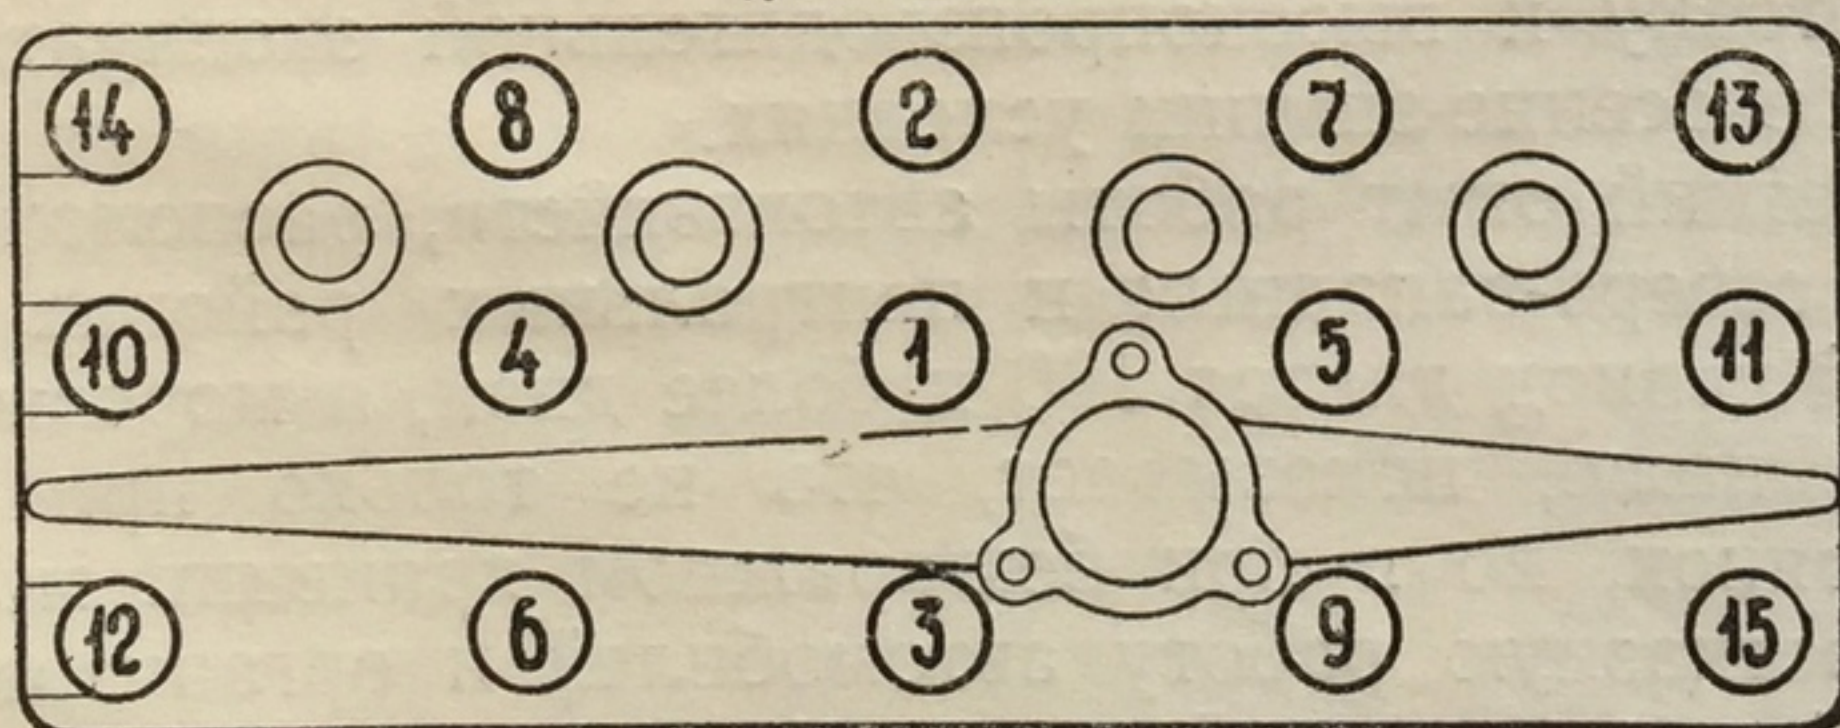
Порядок подтягивания гаек крепления головки блока цилиндров
